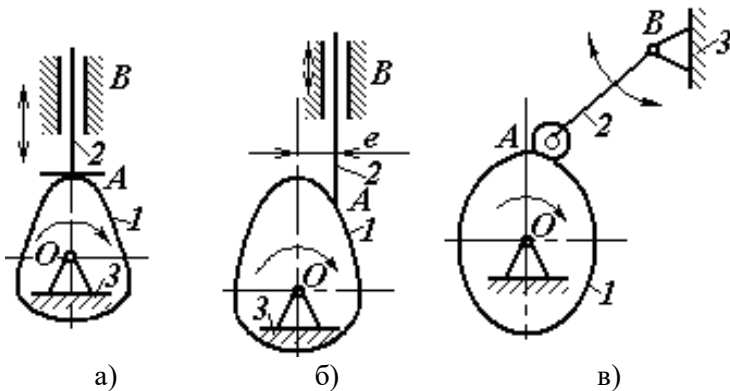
Кулачкові механізми: а, б) з поступальним рухом штовхача; в) з коливальним рухом коромисла
